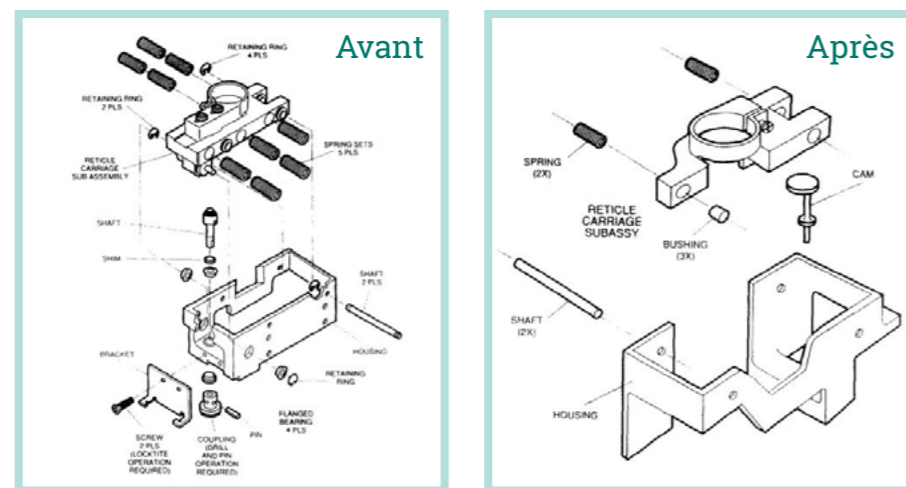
Design For Manufacture and Assembly, aux origines de la conception pour la fabrication additive, extrait de Boothroyd
